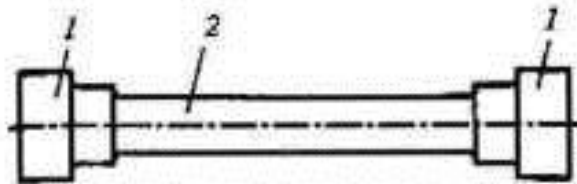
Цилиндрический образец для испытаний на растяжение:
